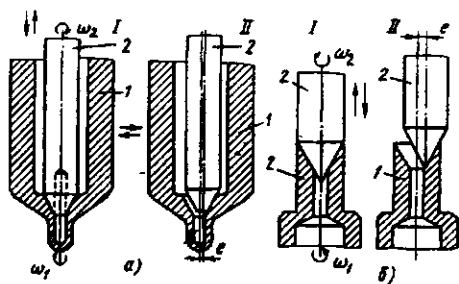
Схемы доводки конических поверхностей по способу ЦНИТА: а и б – для внутренних поверхностей; 1 – деталь; 2 – притир; е – эксцентриситет
